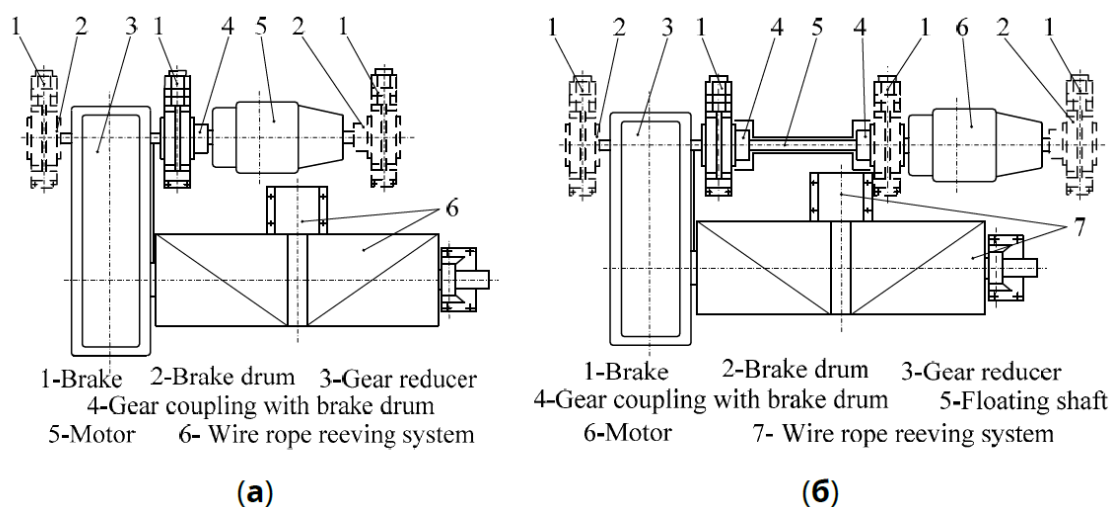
Типова схема механічного гальма в підйомному механізмі мостового крана. (а) Підйомний механізм без плаваючого валу; (б) Підйомний механізм з плаваючим валом.
